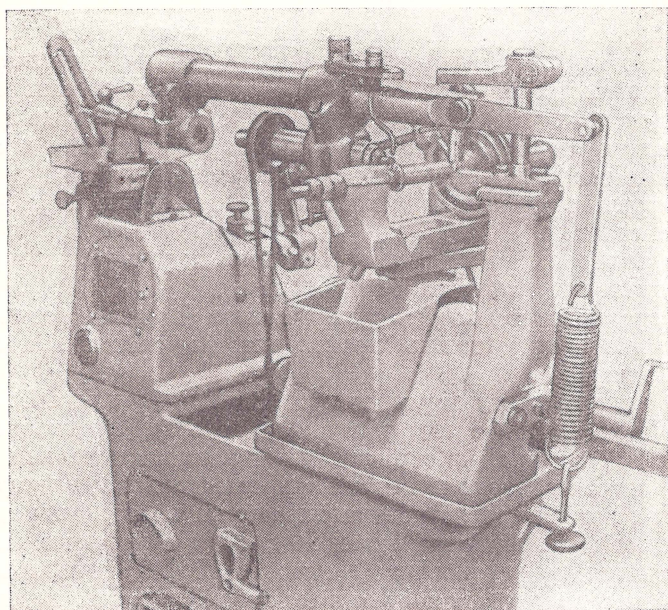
Станок для фрезерования и шлифования затылованных зубьев фасонных фрез
